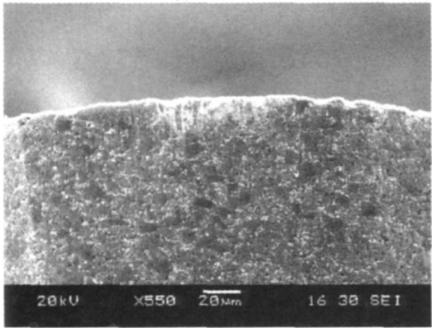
超声波振动切削时 PCD 刀具后刀面磨损形貌(切削路程 300m)
